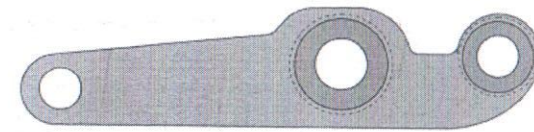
Контроль околошовных зон сварных соединений втулок и соединительных планок с боковинами рычага
